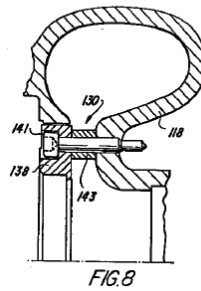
Verschraubung des Trägerringes mit dem Turbinengehäuse, Garrett step-1 [1]
